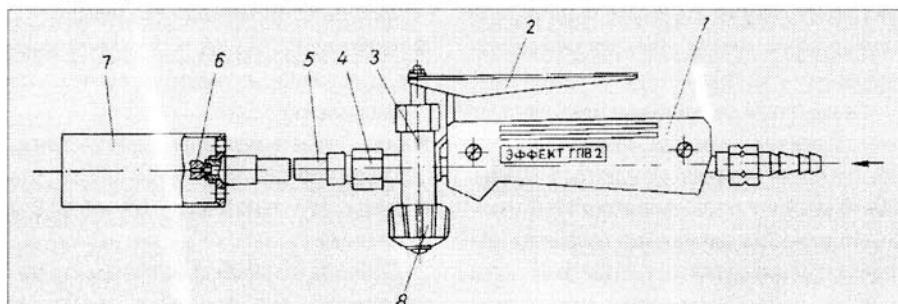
Горелка для укладки кровли, гидроизоляции в печах и других затрудненных для доступа местах:
